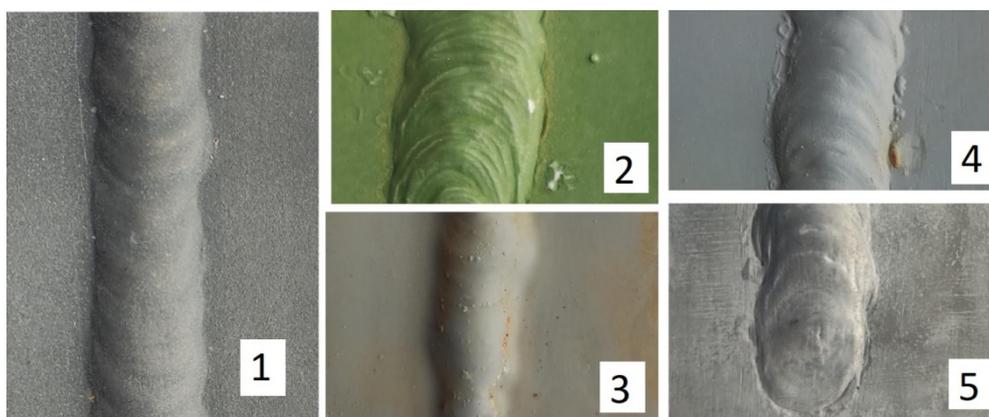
Внешний вид покрытий после проведения испытания: 1 – холодное цинкование; 2 – фосфатирующий грунт; 3 – эпоксидный грунт; 4 – грунт ГФ-021; 5 – гальваническое цинкование с помощью заявленного мобильного устройства
